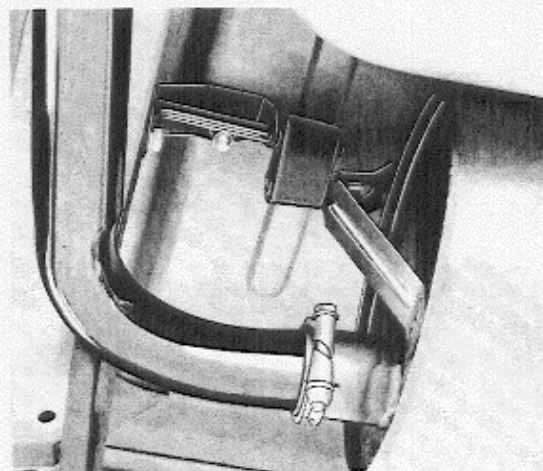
Aufhängung des Nachschalldämpfers (die Aufnahme stammt von 164.)
